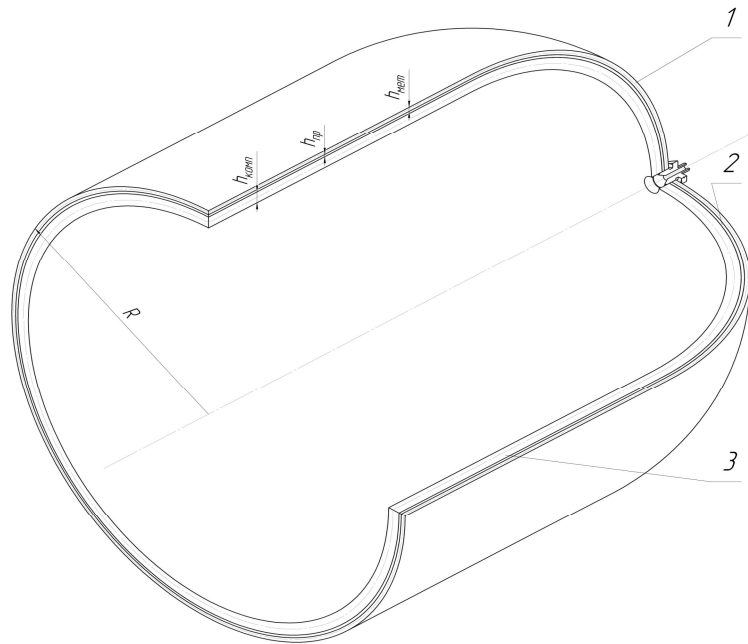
Розрахункова схема комбінованого балона високого тиску: 1 – захисна металева оболонка (матеріал дюралюміній В-95); 2 – податливий прошарок; 3 – склопластикова несуча оболонка
